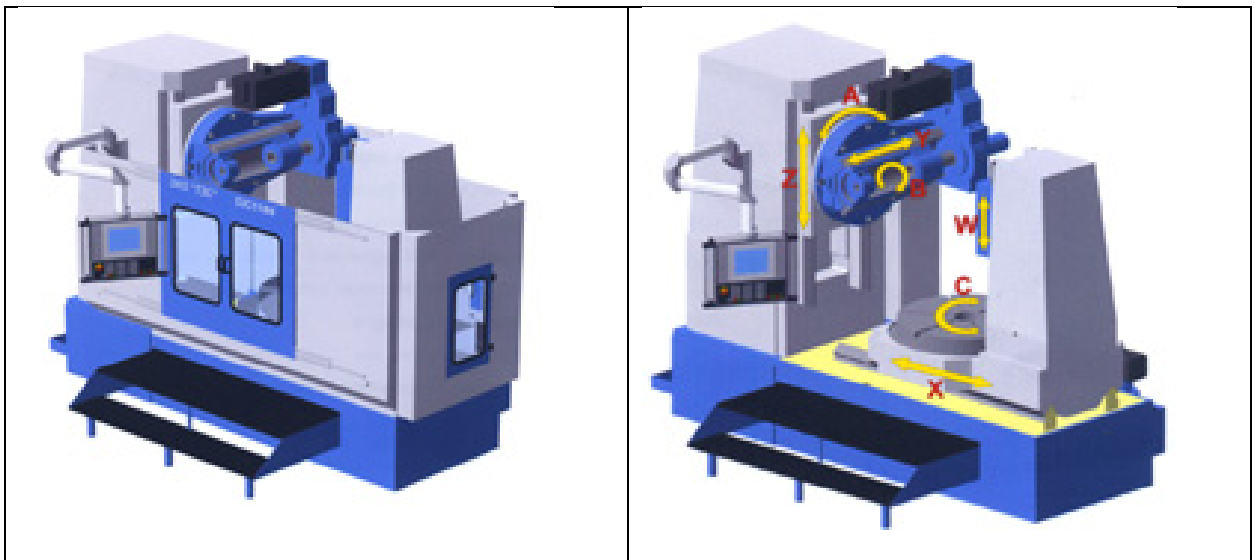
Зубофрезерний верстат з ЧПУ моделі 53С50Ф4
